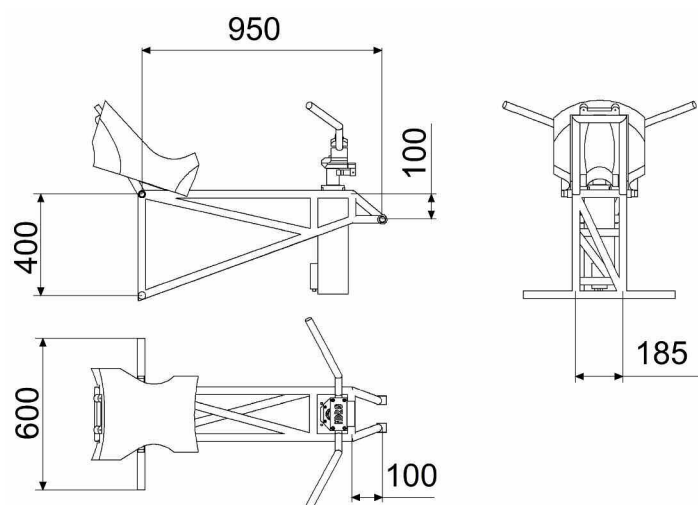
3: Dimensioni di riferimento per il telaio di beccheggio
